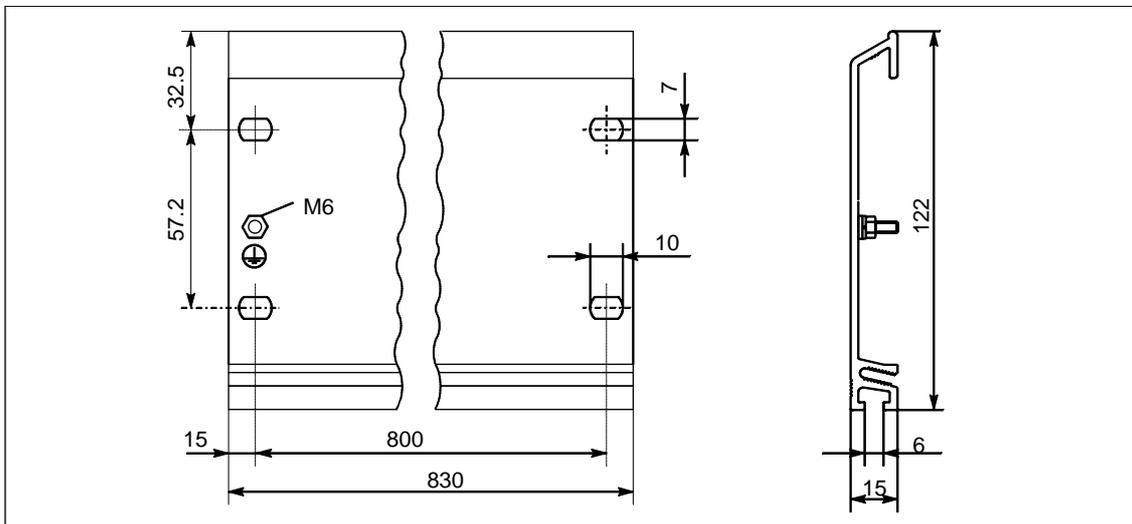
Чертеж с размерами профильной шины стандартной ширины 830 мм
